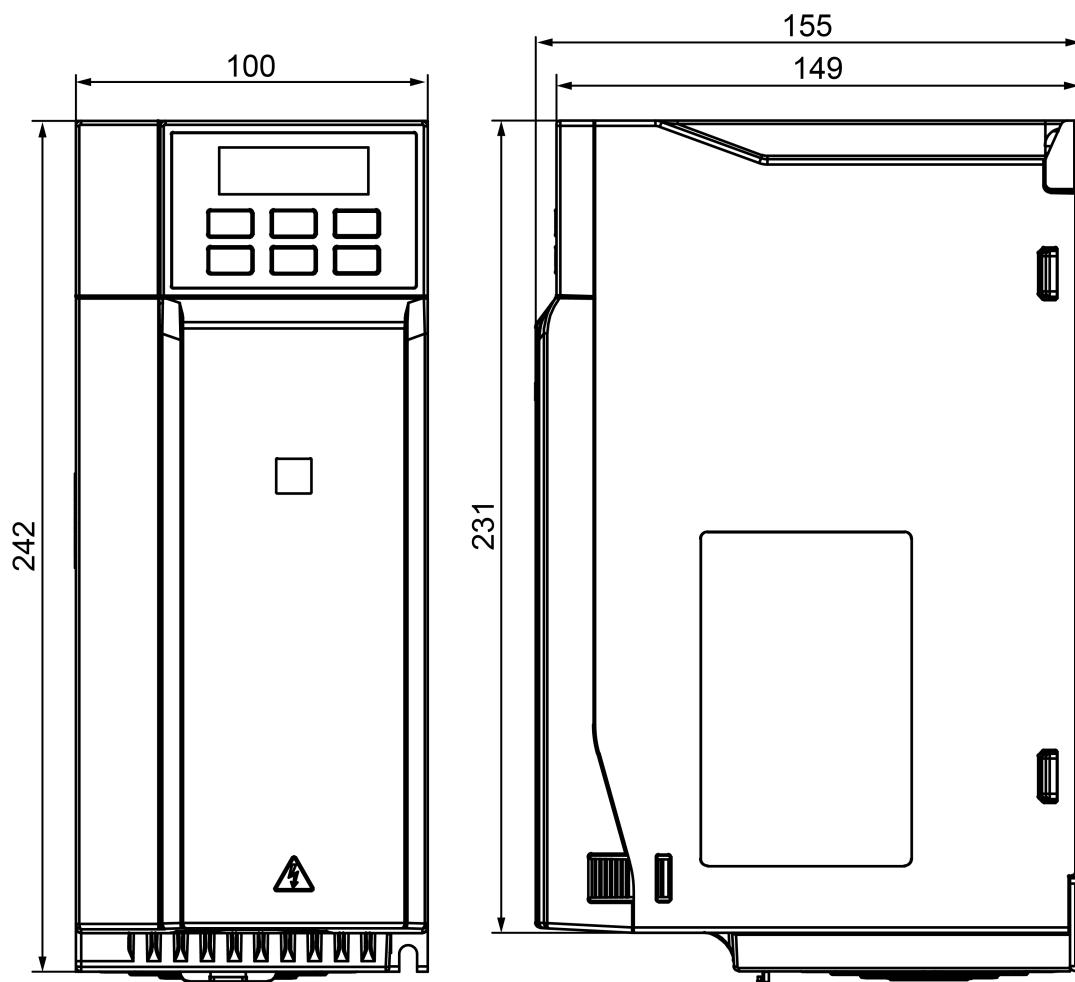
Габаритные размеры прибора в корпусе типоразмера 2
